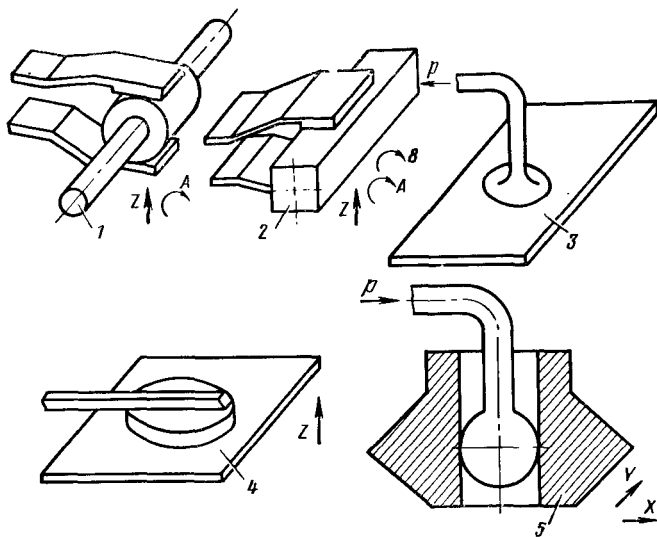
Виды схватов «кисти», «руки» манипулятора для захвата деталей: 1 — цилиндрической; 2 — типа бруска; 3 — плоской (схват с вакуумным устройством); 4 — плоской (схват с магнитным устройством); 5 — с цилиндрическим отверстием (схват с пневматическим устройством)
